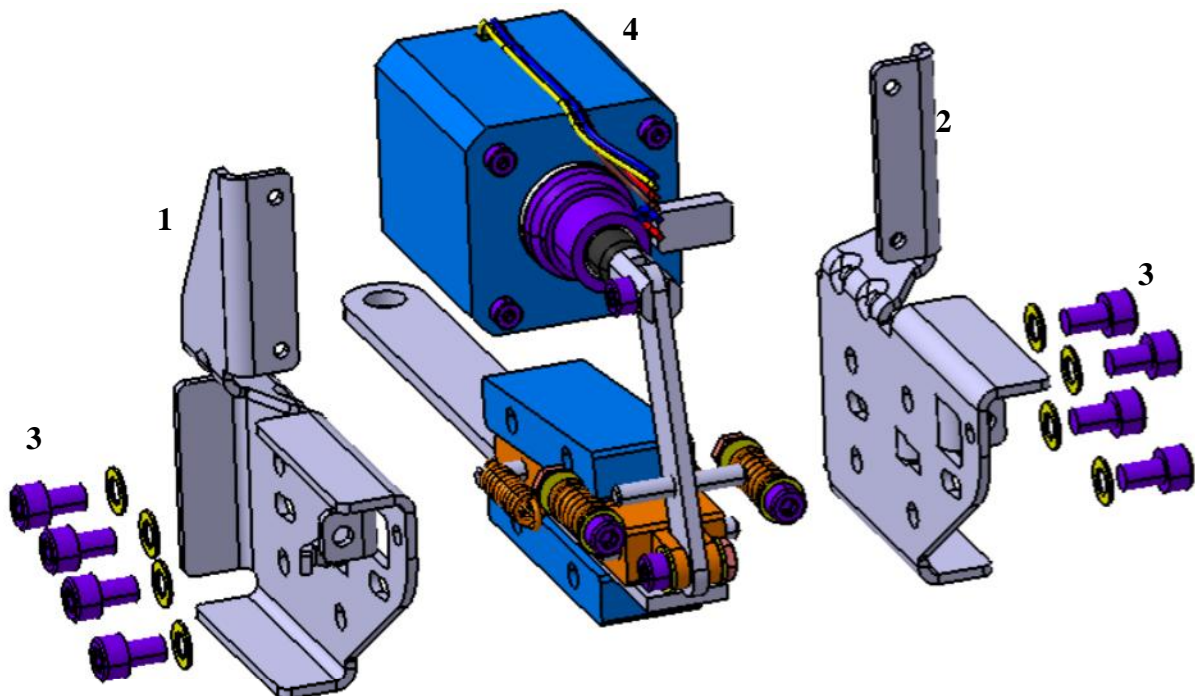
Rozpad sestavy. V Housingu (1) je uložen celý brzdný mechanismus (2), správnou polohu mechanismu v Housingu zajišťují styčné a vodící plochy, které jsou vytvořeny jak na Housingu tak na Coveru (3), tyto dva díly společně přenášejí brzdovou sílu od mechanismu na boční dveře. Cover je k Housingu přišroubován šesti šrouby M4x14 (4).
